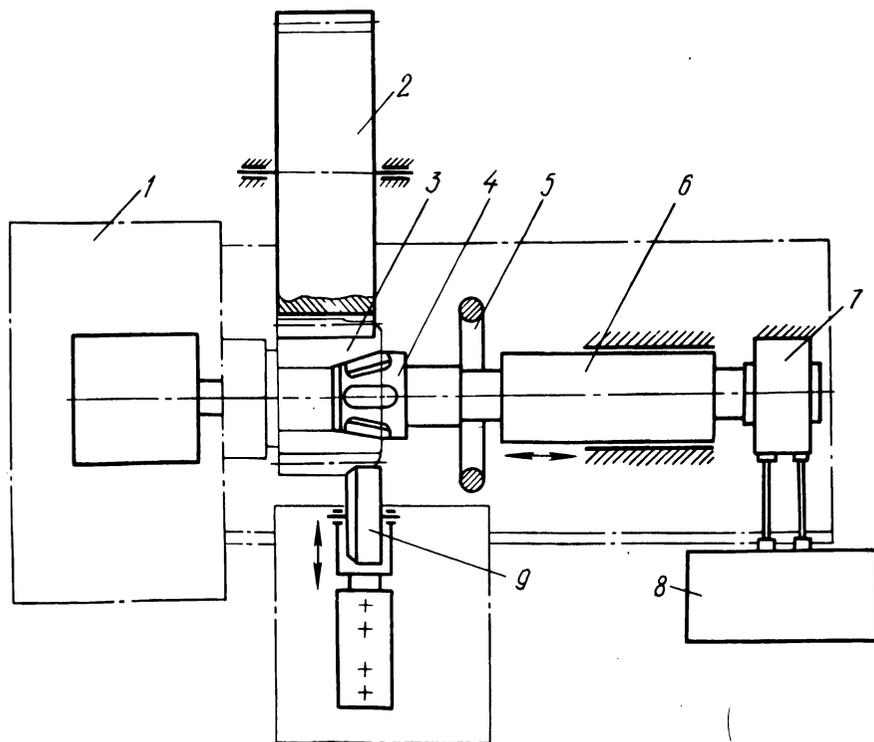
Принципиальная схема установки для восстановления первичного вала-шестерни (дет. 51-7017) коробки скоростей автомобиля ГАЗ-51 методом пластического деформирования.
